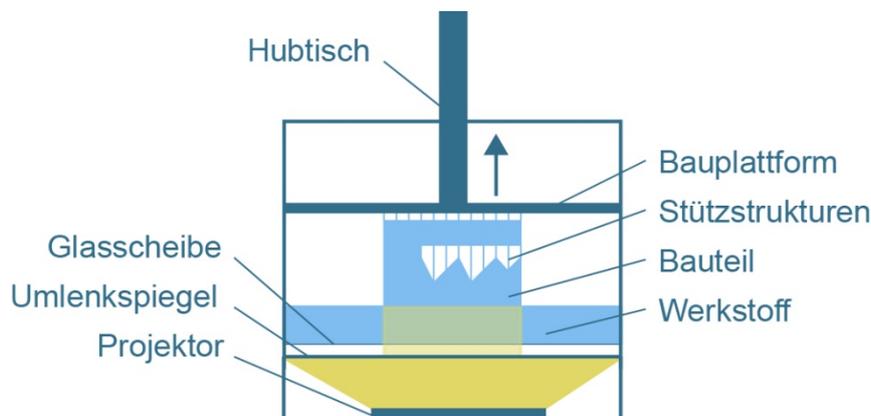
Aufbau und Elemente einer DLP-Anlage
